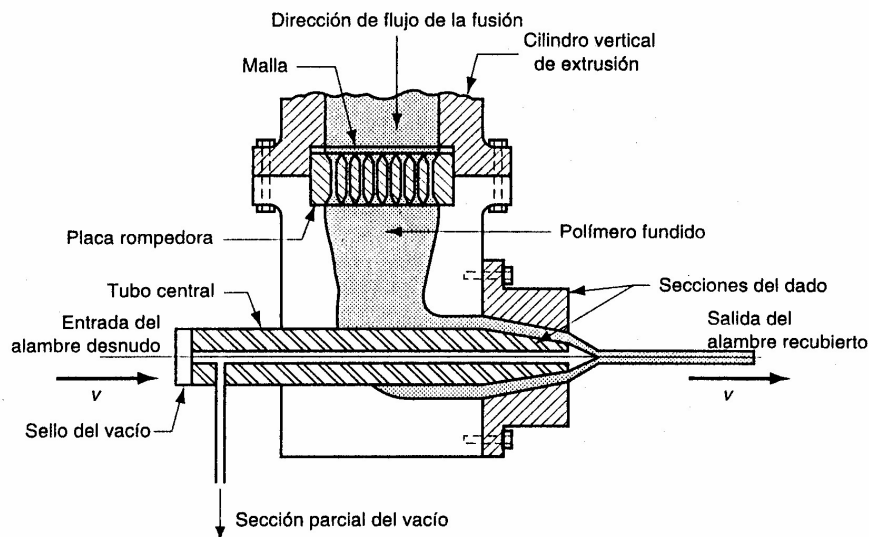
Vista lateral del corte de un dado para recubrimiento de alambre eléctrico por extrusión. Algunos detalles de construcción están simplificados.
